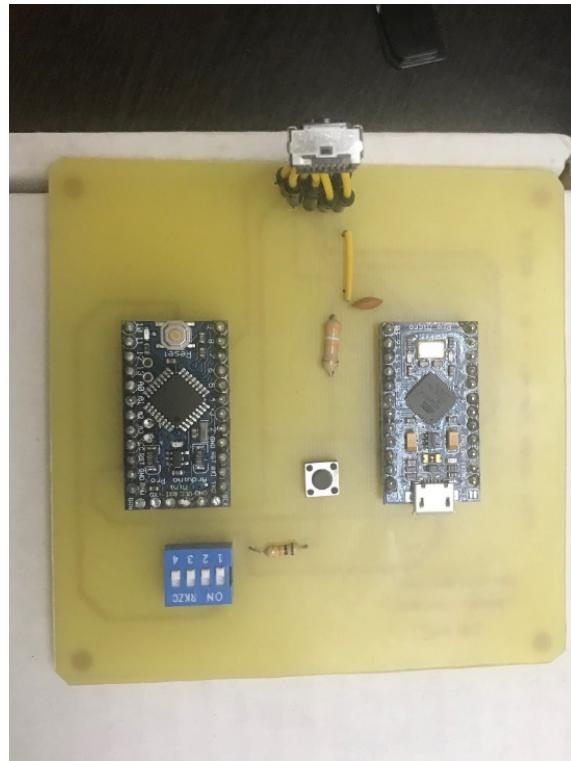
16. Placa de circuito impreso vista desde el lado de los componentes
